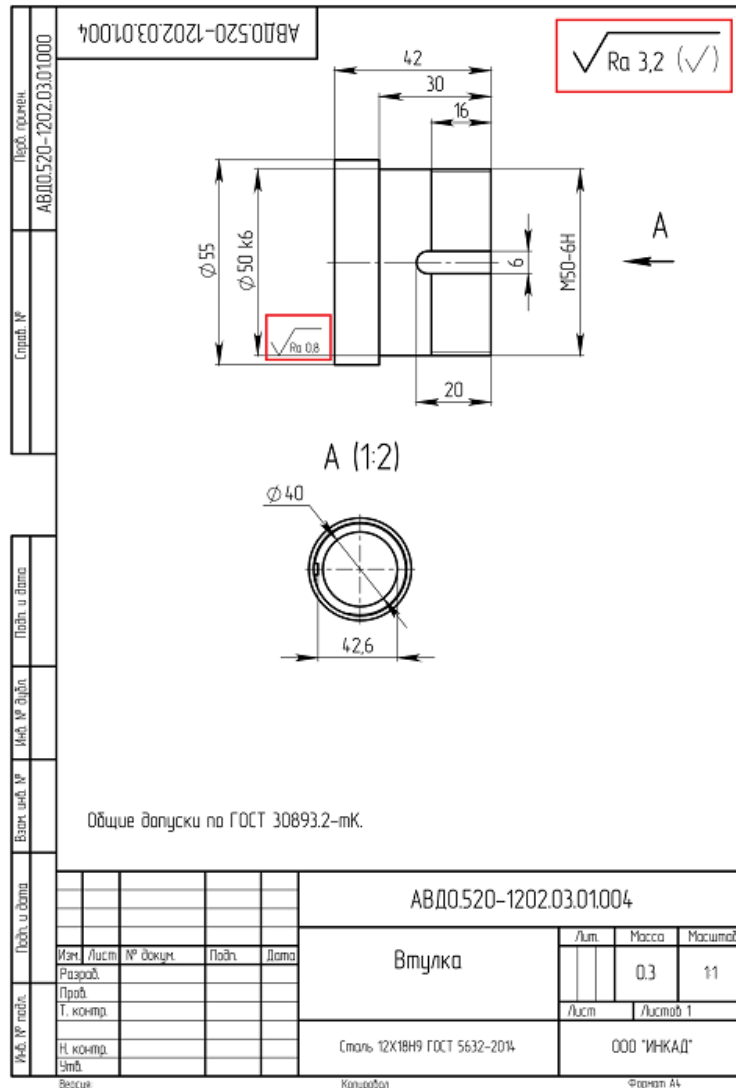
Пример обозначения основной шероховатость на чертеже
